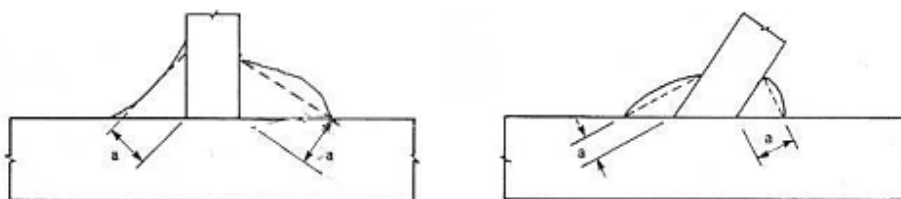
Definição da espessura do cordão de uma soldadura de ângulo (NP EN 1993-1-8, 2010)
